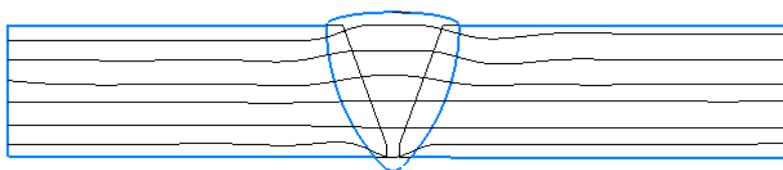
Распределение напряжений в сварном шве с плавным переходом к основному металлу
